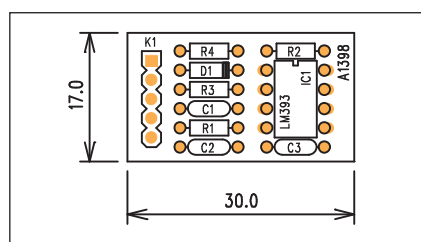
Obrazec desky spojů dotykového alarmu (strana BOTTOM)
